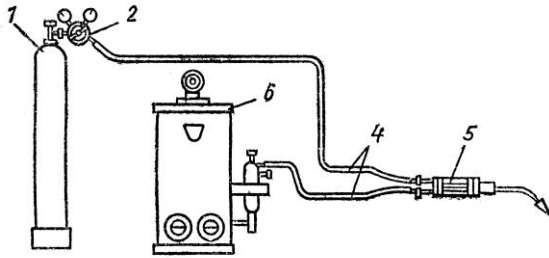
Схема поста газового зварювання: 1 – балон з киснем; 2 – кисневий редуктор; 3 – затвор; 4 – шланги; 5 – пальник; 6 – ацетиленовий генератор
